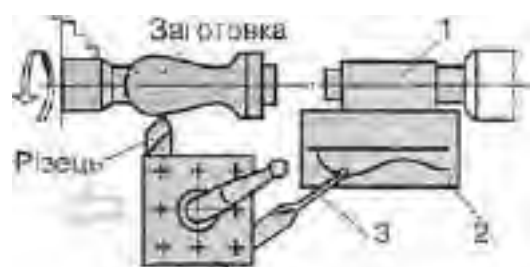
ОБРОБКА ФАСОННИХ ПОВЕРХОНЬ СПОСОБОМ ПОЄДНАННЯ ДВОХ ПОДАЧ З КОНТРОЛЕМ ЗА КРЕСЛЕННЯМ
